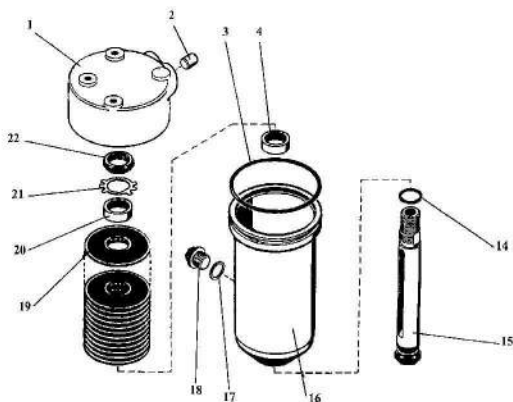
Фильтр коробки передач с напорным клапаном: 1 — корпус; 2 — заглушка; 3, 14 — кольцо; 4, 20 — втулка; 15 — основание; 16 — станок; 17 — прокладка; 18 — пробка; 19 — фильтрующий элемент; 21 — шайба; 22 — гайка.
